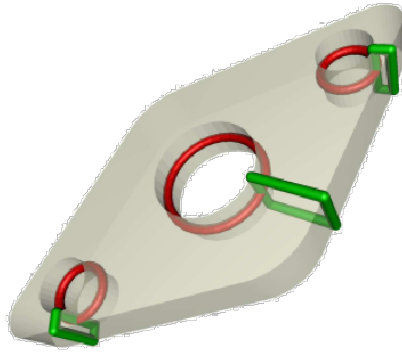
CAD 工件: 红色圈为洞圈, 绿色圈为柄圈
